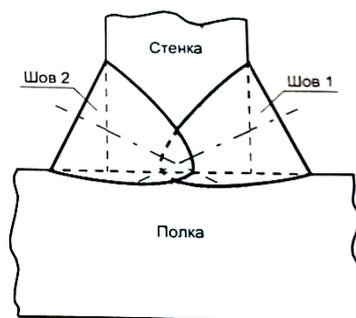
Схема таврового сварного соединения с полным проваром соединяемых деталей
